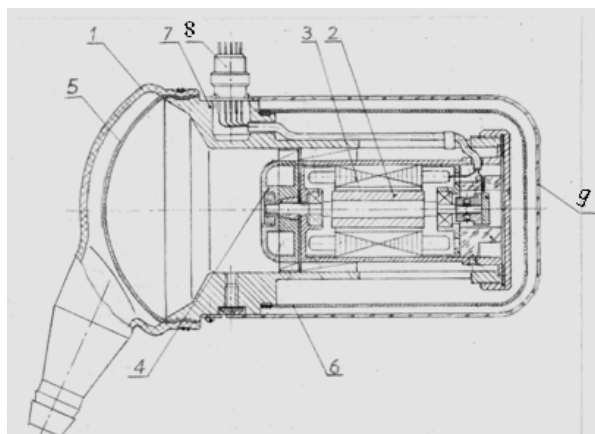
Устройство КИЖ СЭ «Оникс-4М»: 1 – корпус НУК; 2 – магниты ротора; 3 – статор; 4 – импеллер; 5 – диафрагма; 6 – полиуретановая оболочка; 7 – основная втулка; 8 – электроразъем; 9 – кожух
